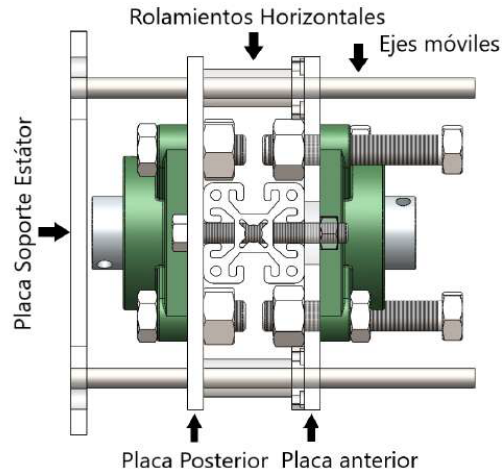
Integración de los elementos de rodamiento del rotor [8].
